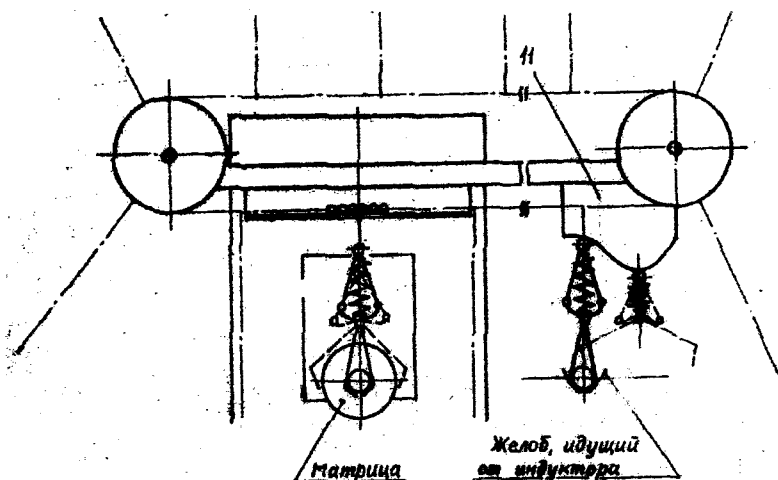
Раскрытие клещей для захвата нагретой заготовки от индуктора
